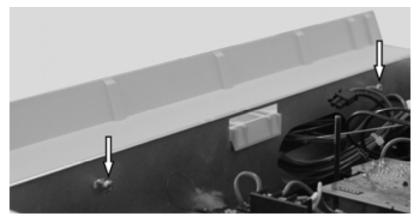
Das Kesselschaltfeld (ohne Regelung) von der Rückseite des vorderen Verkleidungsbleches mit zwei Blechschrauben befestigen.
